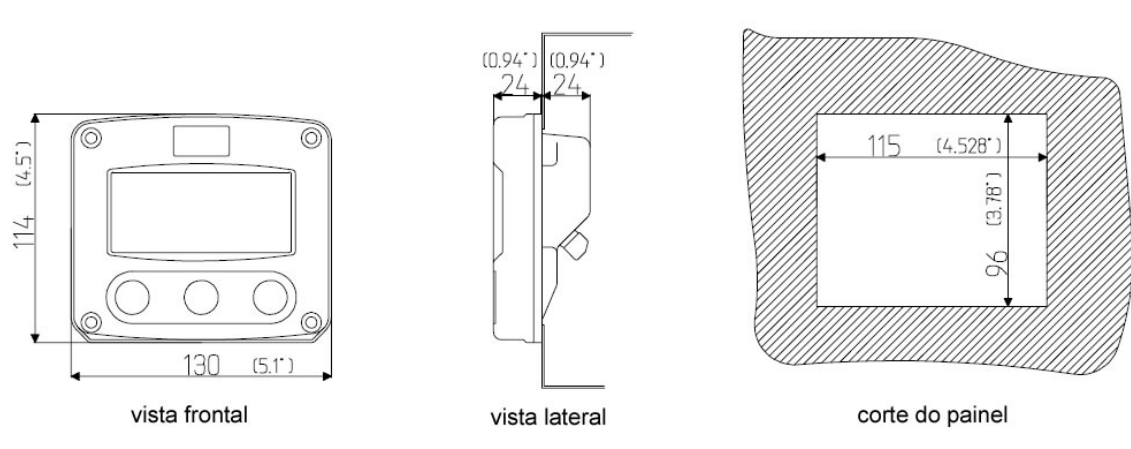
Dimensões do Invólucro padrão IP65 ABS para montagem em painel / corte do painel.
